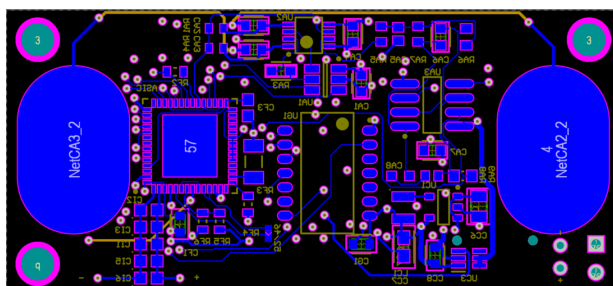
Layout de la PCB final del dispositivo vestible. Solo capa inferior (BOTTOM) visible. Las dimensiones de la PCB son $55\text{mm} \times 25\text{mm}$. Esta capa contiene a en ambos extremos (izquierda y derecha), los PADs de soldadura de electrodos. En el espacio restante entre PADs se dispone el canal ECG (arriba), el ASIC (izquierda), el RTC externo utilizado por el ASIC (centro) y parte del PMC (dercha).
